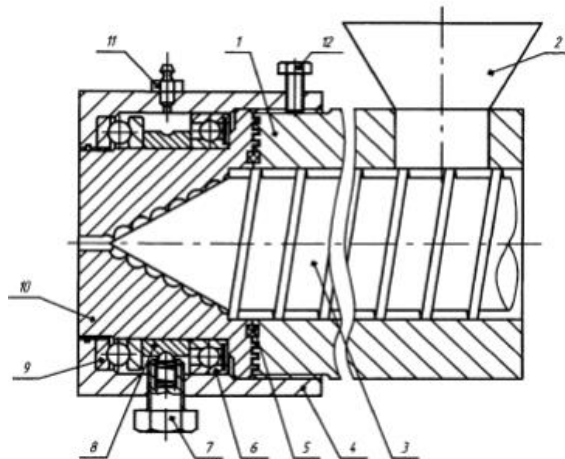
Екструдер з матрицею, що гасить пульсації тиску: 1 – корпус; 2 – завантажувальний пристрій; 3 – шнек; 4 – гільза; 5 – чепцеве ущільнення; 6, 9 – підшипники; 7 – притискний пристрій; 8 – втулка; 10 – формувальна головка; 11 – маслянка; 12 – стопорний болт.
